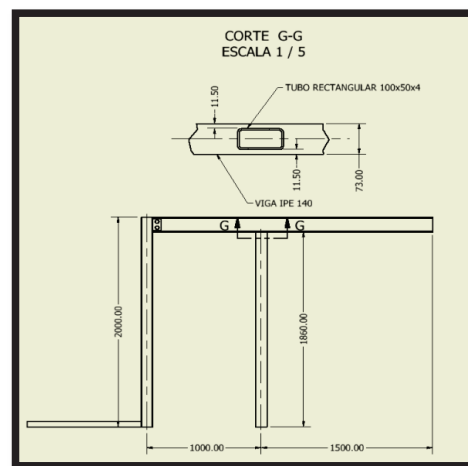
Dimensiones disponibles entre la viga de carga y la columna frontal.
